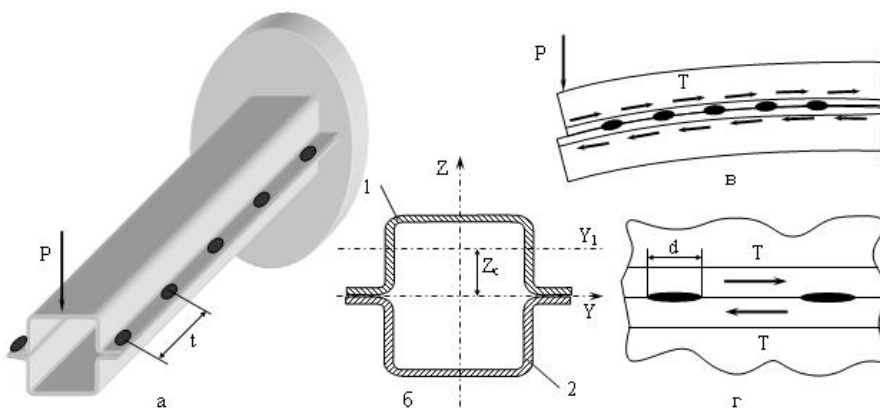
Схема расчет сварных точечных соединений, нагруженных касательными силами при поперечном изгибе балки.
